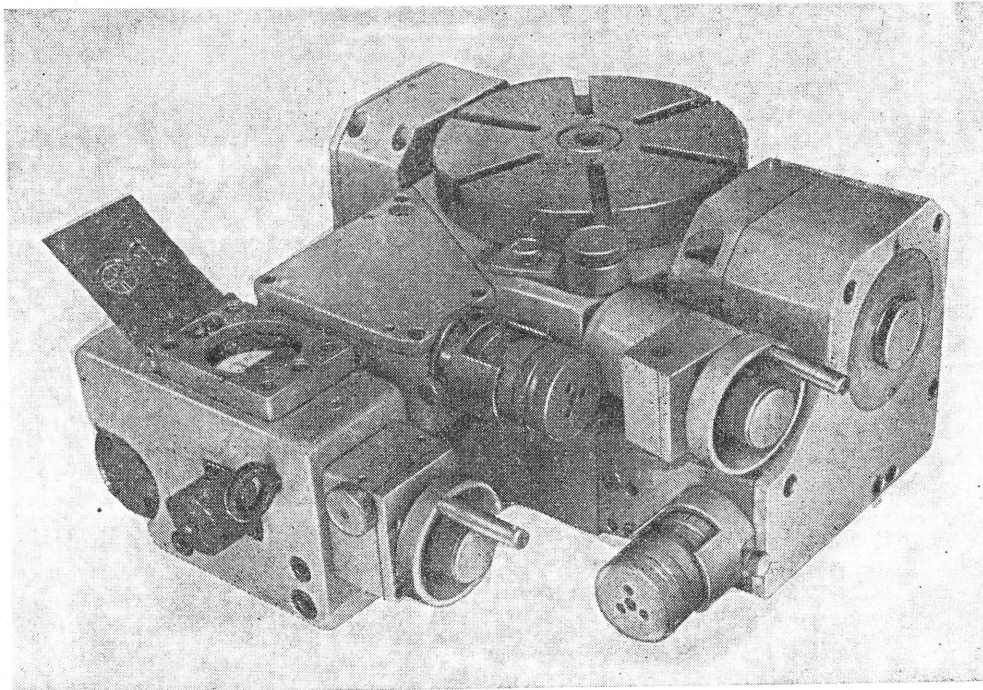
Стол универсальный поворотный делительный координатно-расточных станков
